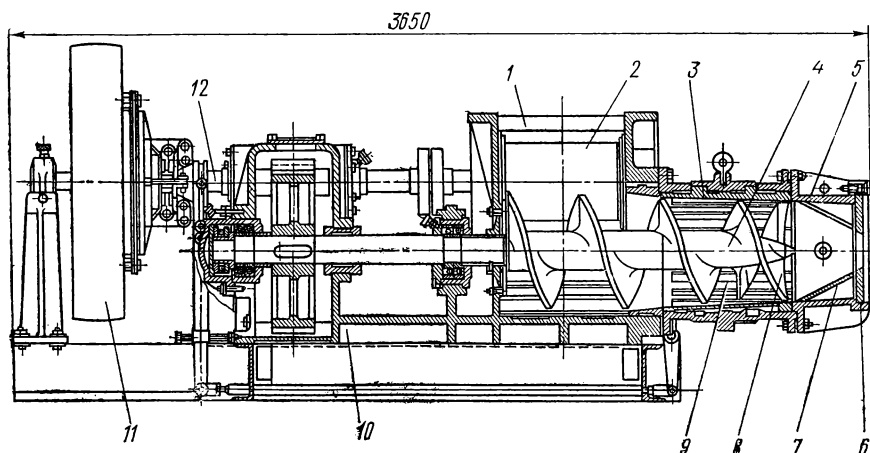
Безвакуумный ленточный пресс СМК-21:
